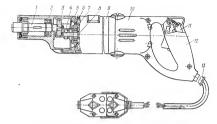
Ручная сверлильная электрическая машина ИЗ-1013: 1— шпиндель; 2— кормус редукторы; 3— ведомая шестерыя; 4—блок шестерея; 5— ведущая шестерия; 6— вромежуточный шит; 7— вентильятой; 3— вал роторы; 9— корпус 10— вадкяя крышка; 11— выключатель; 12— основная рукоятка; 13— токоподводящий кабель.
